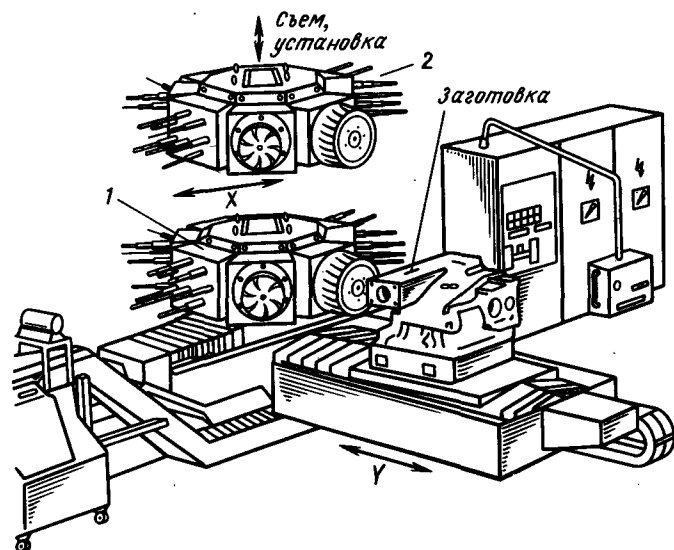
Устройство смены головок. Станок со сменными револьверными головками типа «Вариоцентр» фирмы «Дидисхайм» (по оси X перемещается инструментальная головка, а по оси Y — заготовка):
